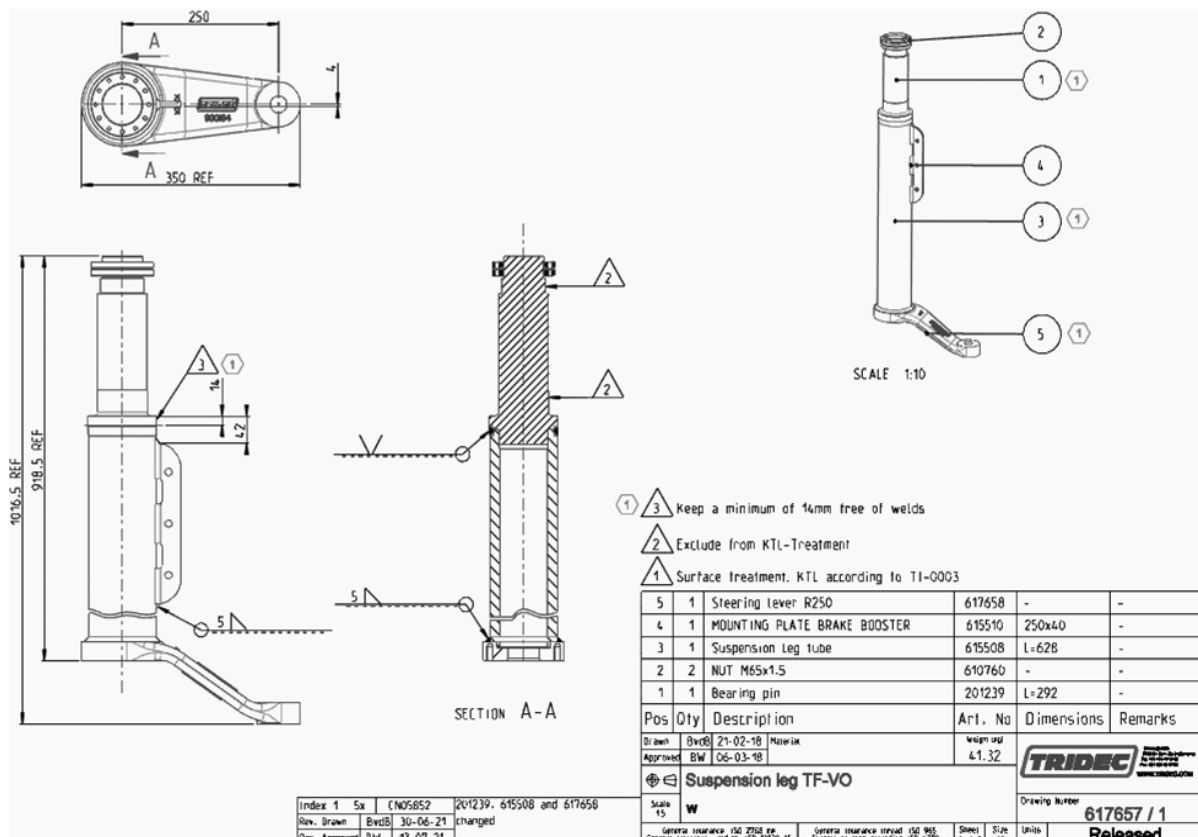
Desenho 2D de uma peça de soldadura
